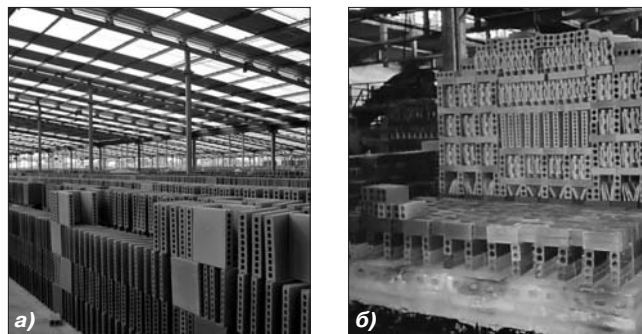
Вид садки крупноразмерного сырца керамических изделий: а – укладка двойных плиток размером 400×400×50 мм на крытой широкопролетной площадке с композитной кровлей; б – оптимальный вариант совместной садки двухпустотного кирпича, плитки для пола и разной черепицы
